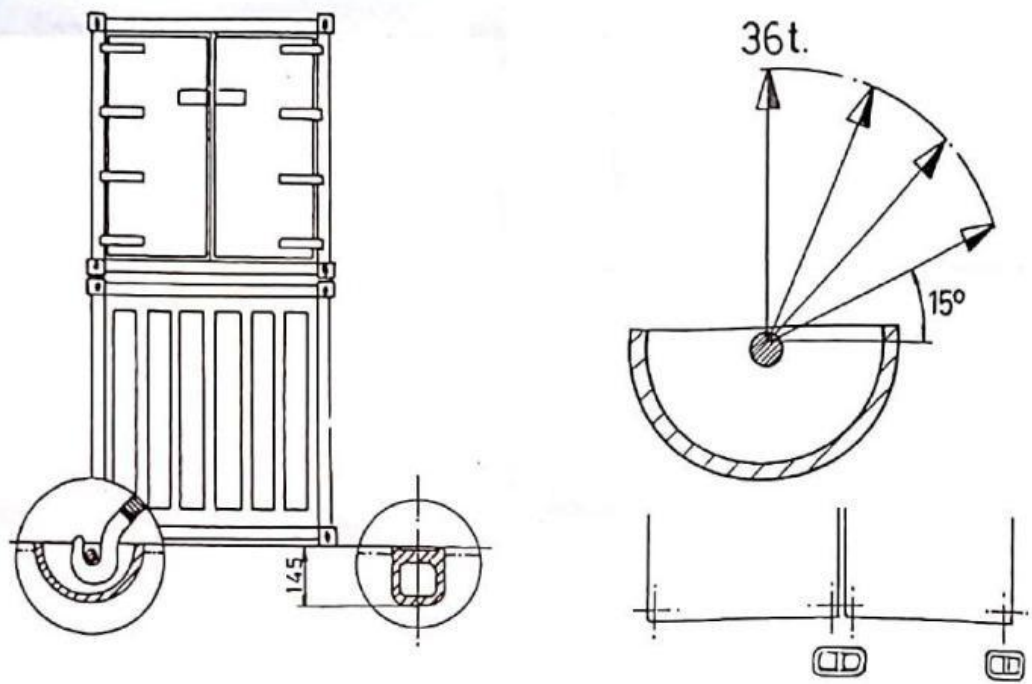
Fundamento para trinca de gancho.
